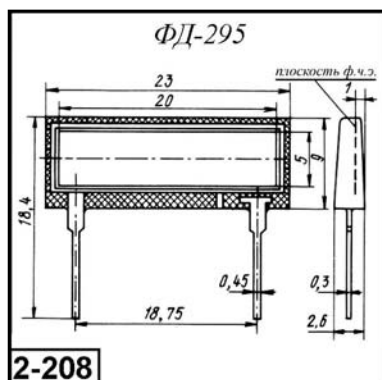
Внешний вид, габаритные размеры кремниевых фотодиодов
